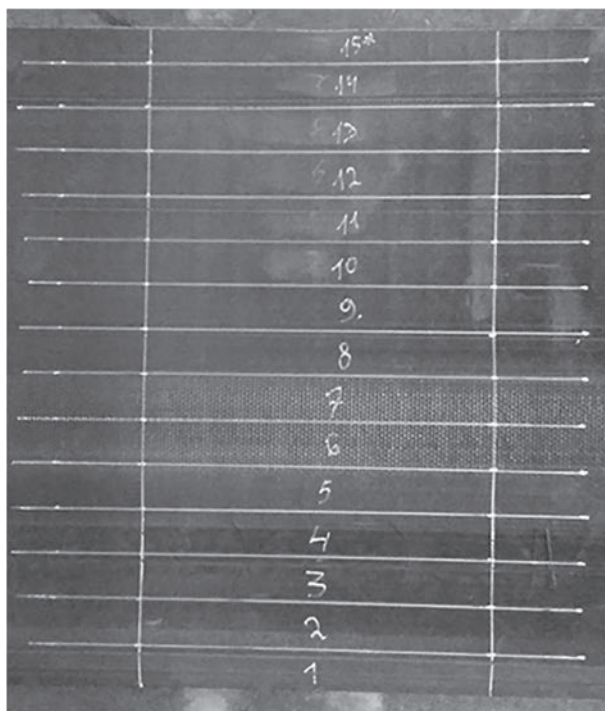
Нанесение разметки по ширине и длине на детали боковины до сборки шины
